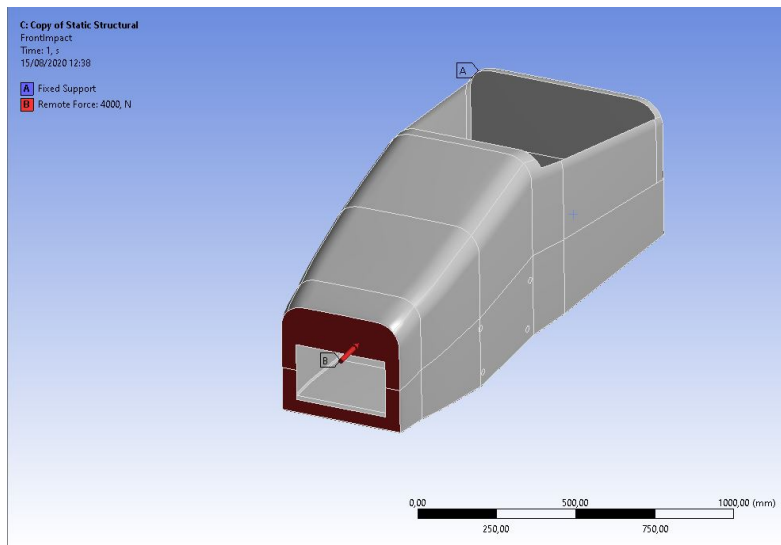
Condiciones del ensayo de impacto frontal del monocasco.
